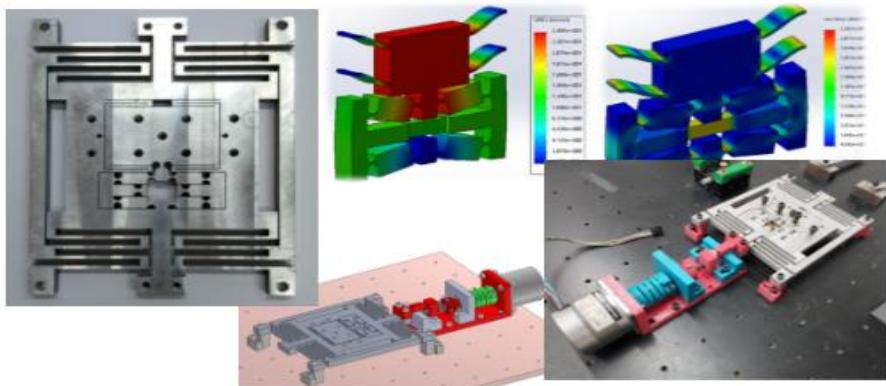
Diseño y montaje del posicionador dual de alta resolución.
